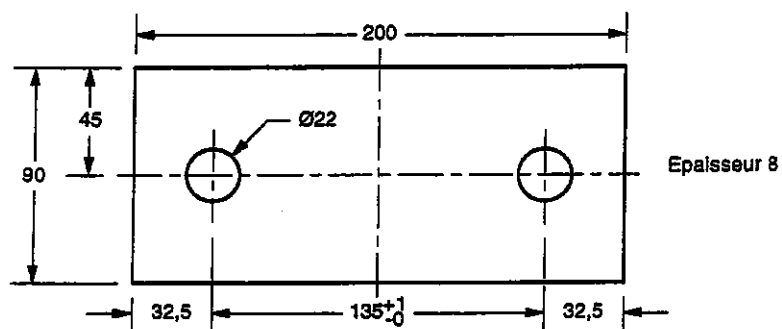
Liaison barrière BN4-glissière — Plat de bridage
